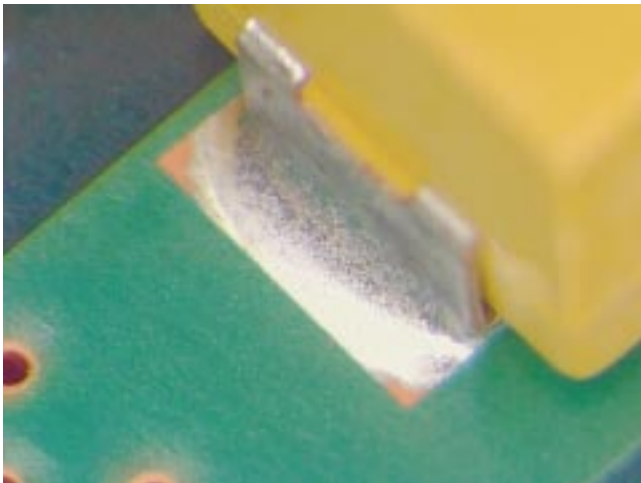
Soldadura SnPb; Flux Soluble en Agua
